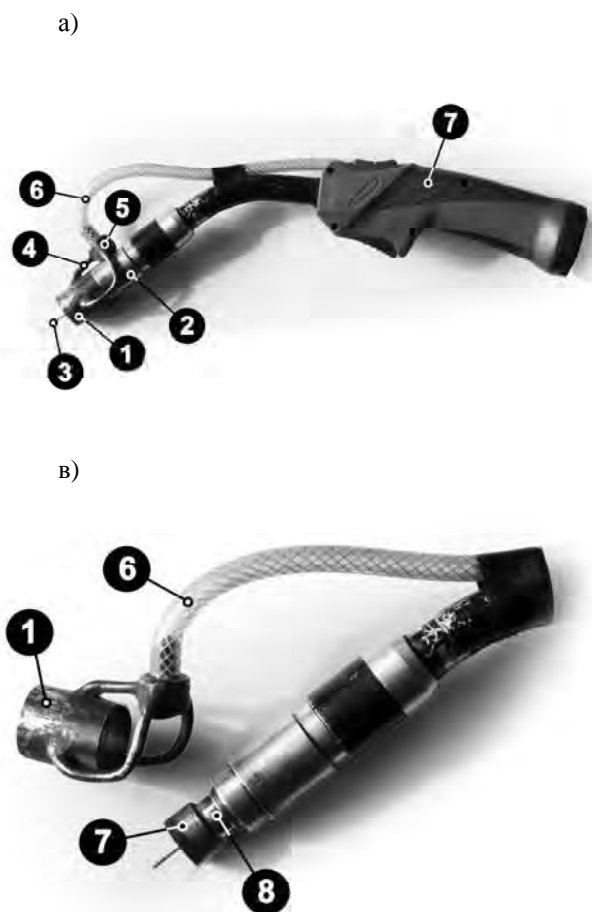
Внешний вид сварочной горелки (а) и элементы сопла с коаксиальной двухструйной подачей защитных газов в зону сварки (б): 1 – внешняя съемная часть сопла; 2 – сопло сварочной горелки; 3 – электродная проволока; 4 – газоподводящие трубки; 5 – газораспределительный штуцер; 6 – шланги для подвода углекислого газа к кольцевому каналу сопла; 7 – сварочная горелка; 8 – полость для стабилизации потока газа
